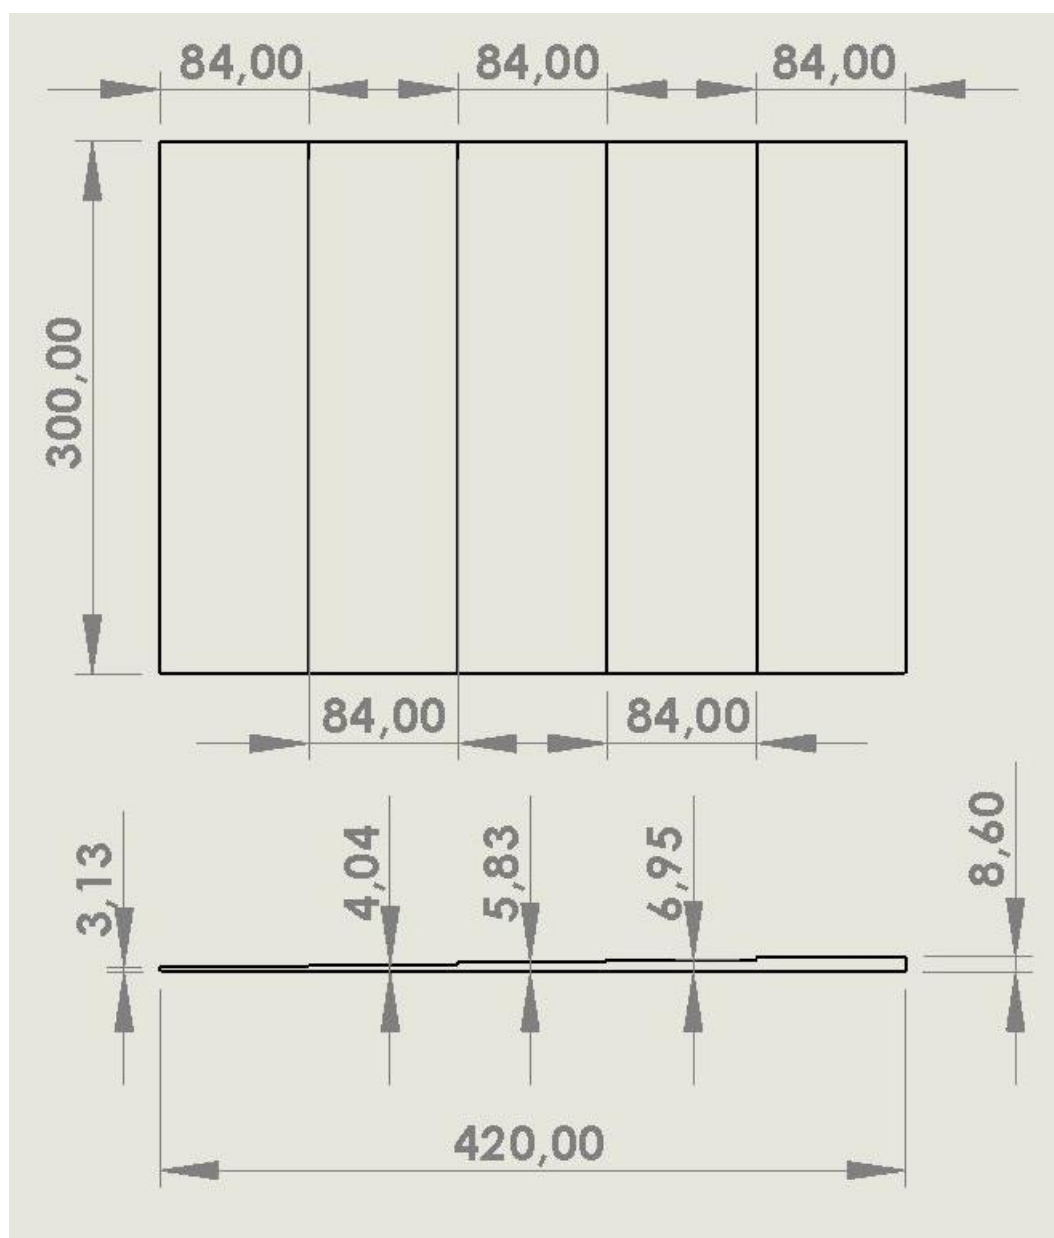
Desenho técnico 2D relativo ao laminado C_1 (dimensões em mm).
